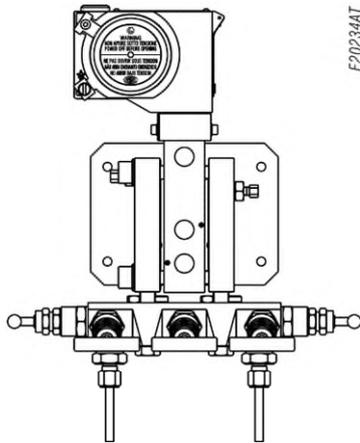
Montaggio valvola manifold con “dado girevole” ½ G
